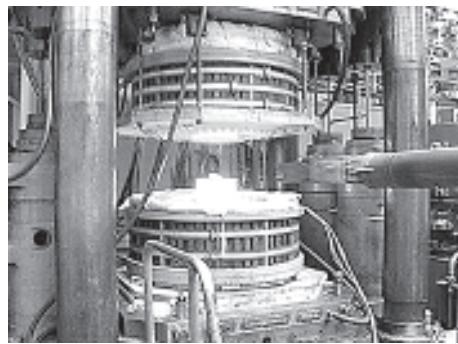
Внешний вид штамповки из пресс-прутка сплава ЭП975 на заключительной операции деформации после подъема выталкивателем из штампа пресса усилием 1600 тс
